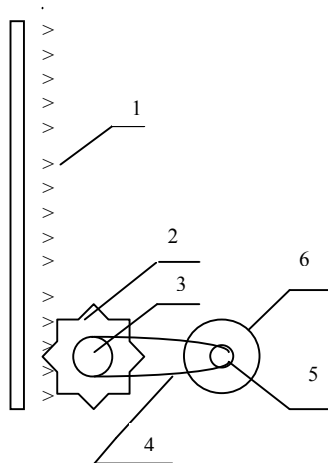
Кинематическая схема механизма автоматической подачи семян: 1 – рейка зубчатая; 2 – шестерня реечная; 3 – шкив ведомый; 4 – ременная передача; 5 – шкив ведущий; 6 – электродвигатель
